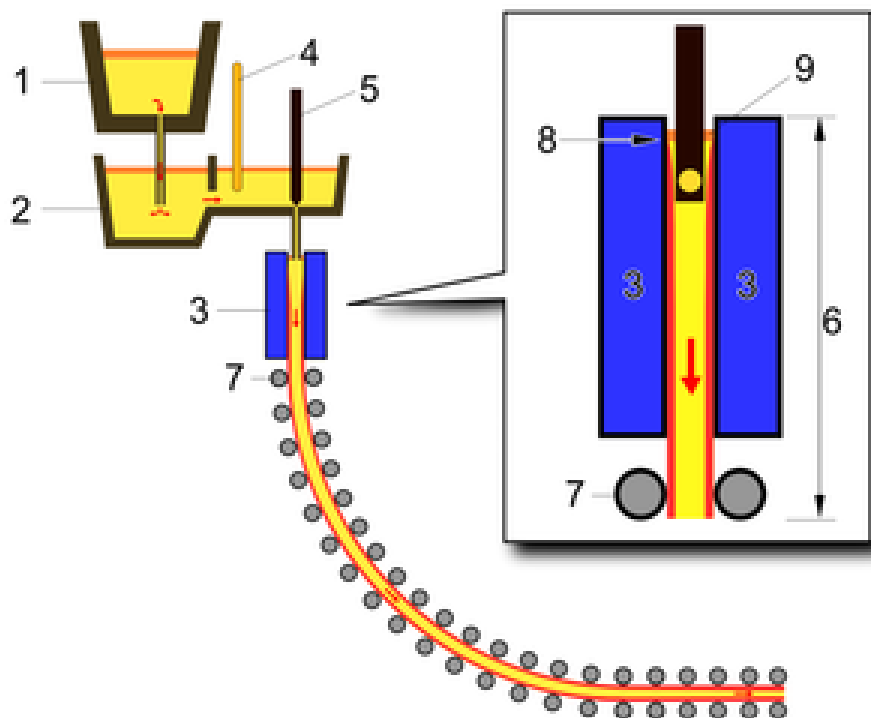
Схема установки безперервної розливки сталі:
